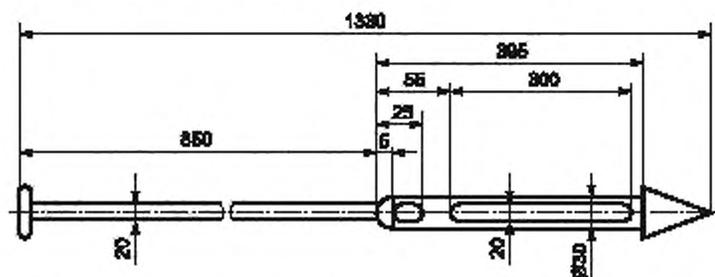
Внешний вид ручного щелевидного пробоотборника
